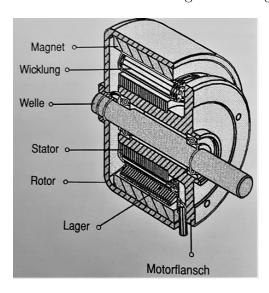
Schnittbild eines BLDC-Motors in Außenläuferausführung (Quelle: [2, S. 76])
